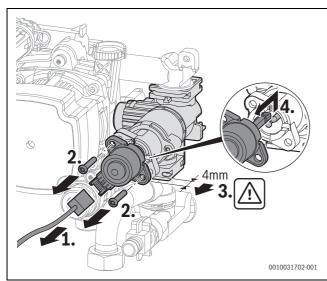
Smontaggio del motorino dalla valvola a 3 vie Montare il motorino.
